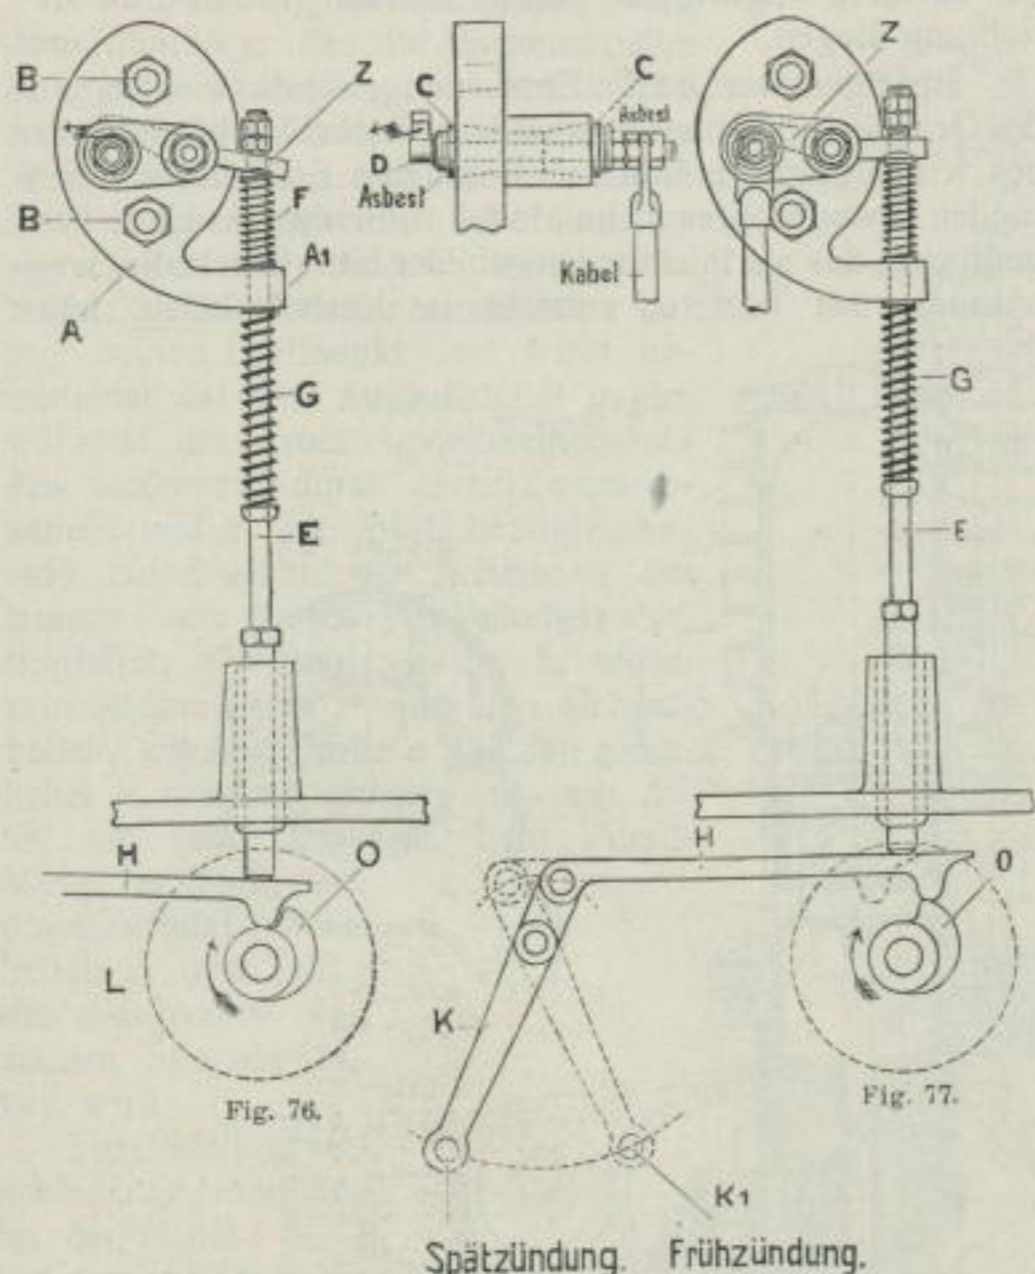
und 77. Steuerung für die Zündung beim Motor, System Laurin & Klement.
